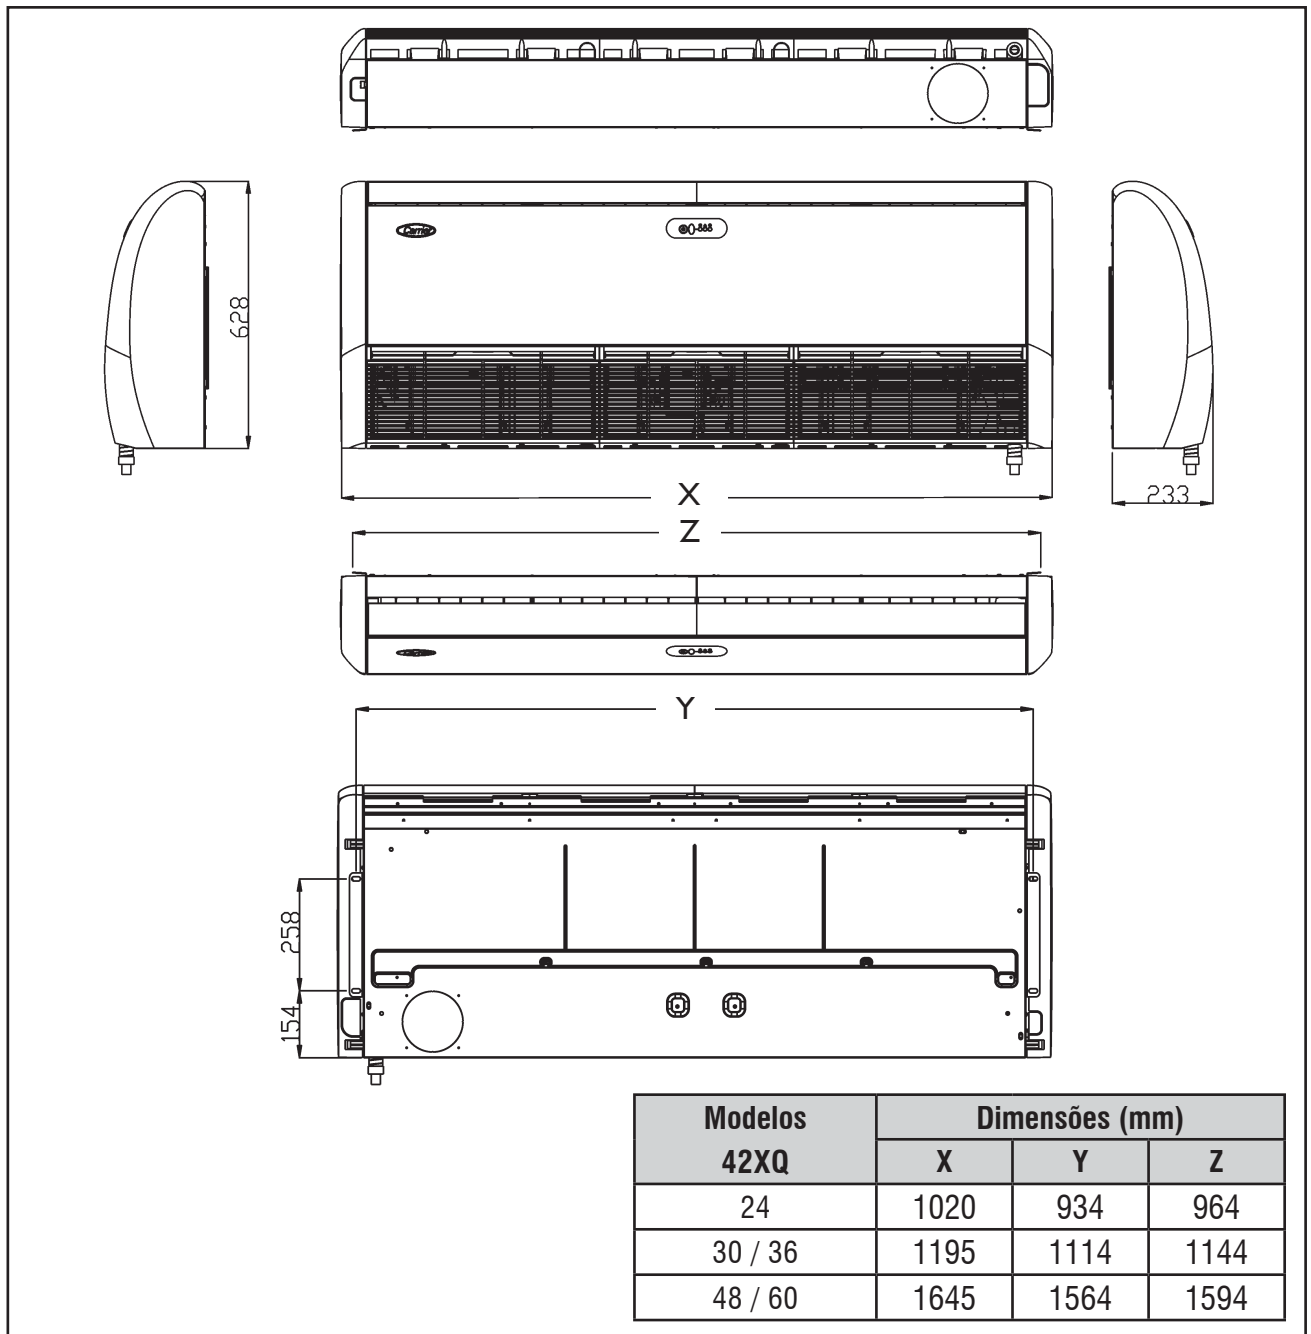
DIMENSIONAL UNIDADE EVAPORADORA
